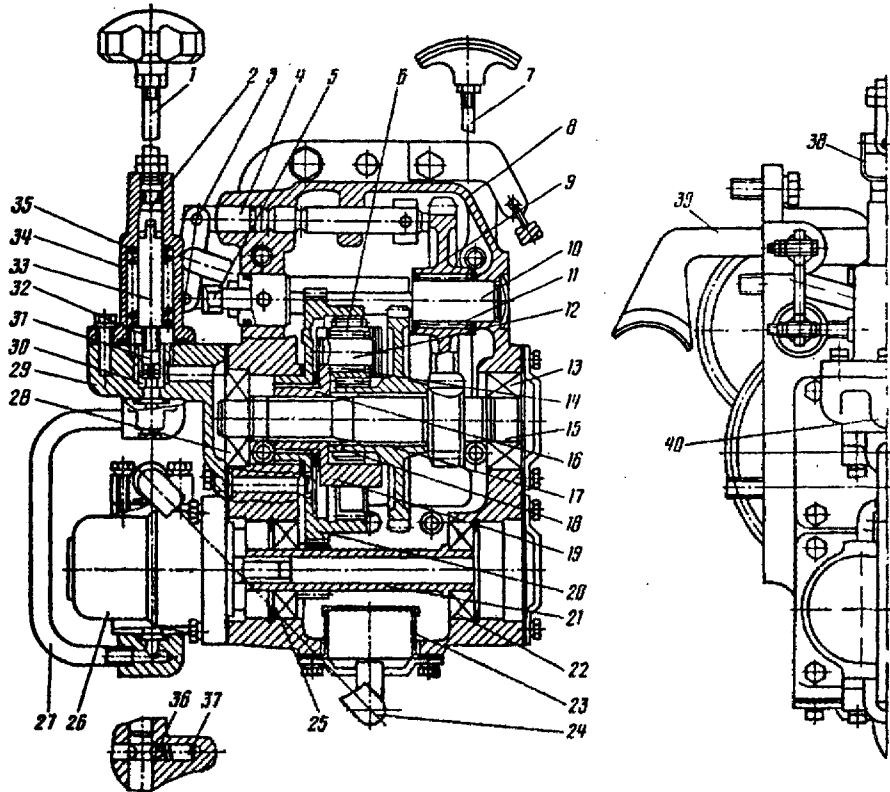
Гидроходоуменьшитель тракторов семейства МТЗ: 1 — стержень управления дросселем; 2, 33 — винты; 3 — рычаг управления; 4 — валик управления; 5 — вилка регулирования; 6 — сателлит; 7 — тяга управления; 8 — корпус; 9 — Промежуточная шестерня; 10 — ось; 11 — роликовый подшипник; 12 — ось сателлита; 13, 22, 25 и 28 — подшипники; 14 — ролики сателлитов; 15 — вал-шестерня; 16 — втулка коронной шестерни; 17 — втулка солнечной шестерни; 18 — солнечная шестерня; 19 — водило; 20 — коронная шестерня; 21 — вал-шестерня привода насоса; 23 — заборник; 24 — всасывающий маслопровод; 26 — насос; 27 — нагнетательный маслопровод; 29 — корпус дросселя; 30 — седло; 31 — шток; 32 — гайка; 34 — крышка дросселя; 35 и 37 — пружины; 36 — шарик; 38 — карданная муфта; 39 — вилка; 40 — дроссель
